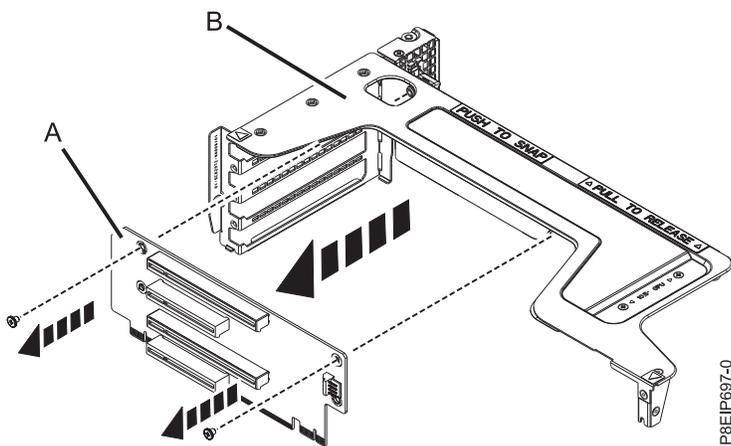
Removendo a placa riser das posições 5, 6, 7 e 8
